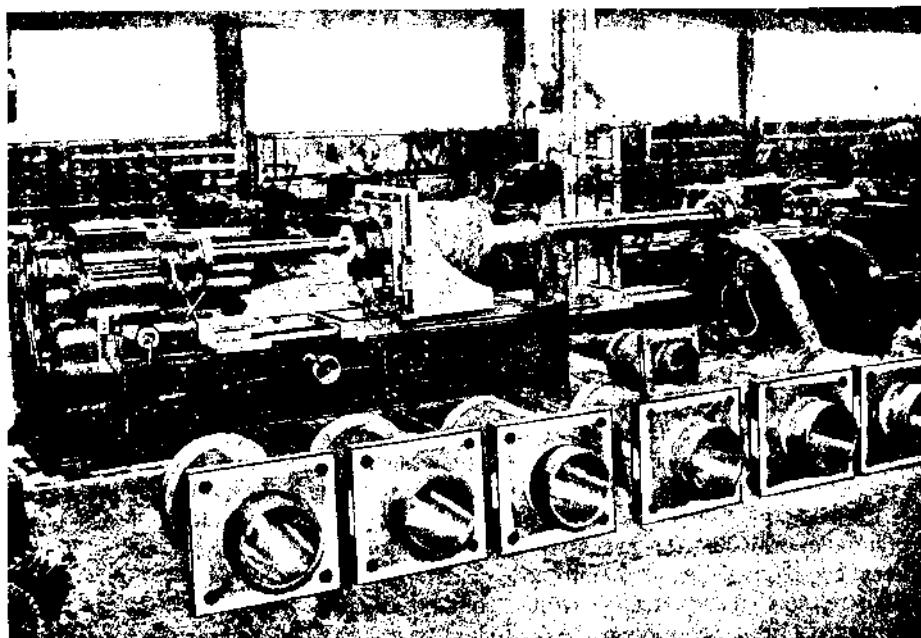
Шлифовка втулок цилиндров дизеля после запрессовки их в рубашки.
